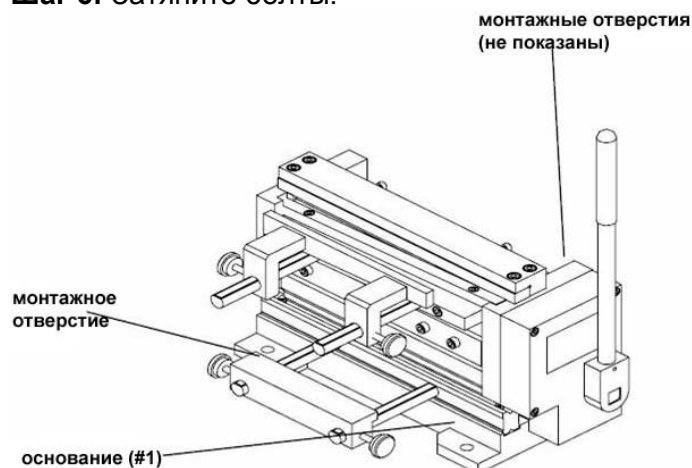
Установка станка для резки/гибки на деревянный верстак
